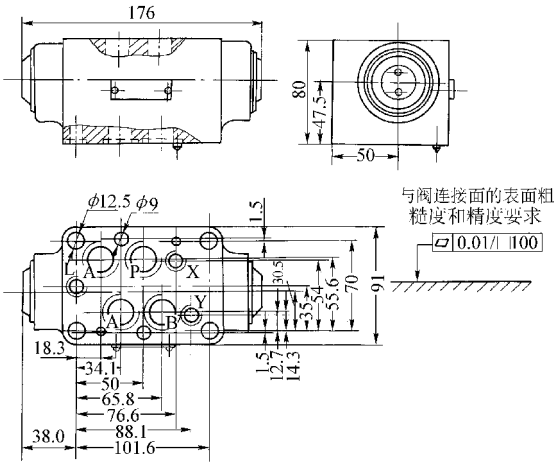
Z2S-16 型叠加式液控单向阀的外形尺寸
